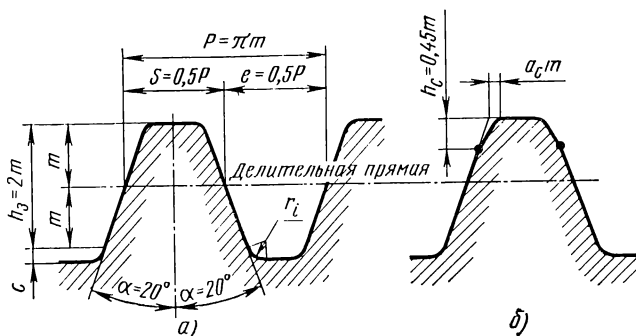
Исходный контур цилиндрических зубчатых колес: а — форма и размеры контура, б — контур с модифицированным профилем
